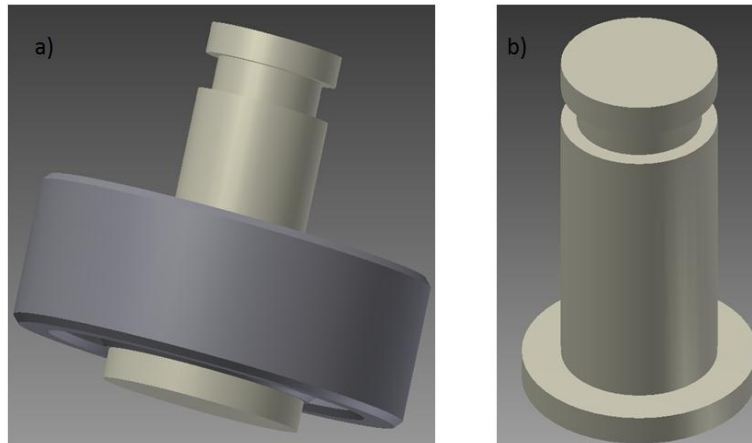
Eje del seguidor. a) Con rodamiento b) Vista isométrica
